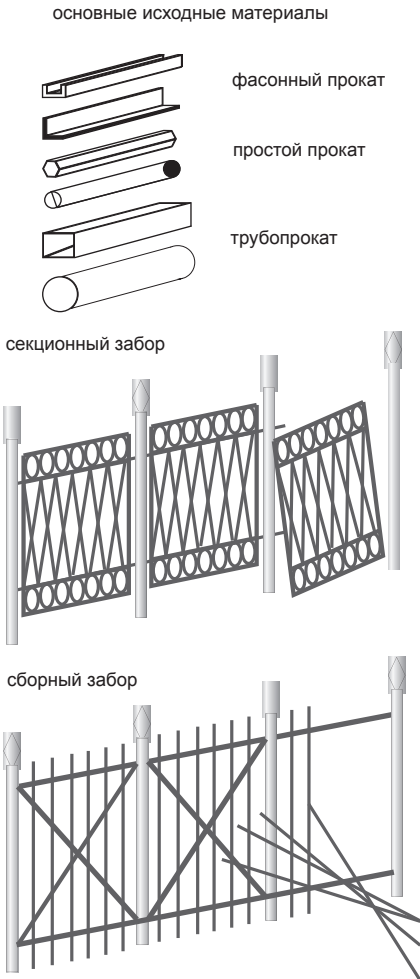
Детали для сборки сварных ограждений и способы монтажа
